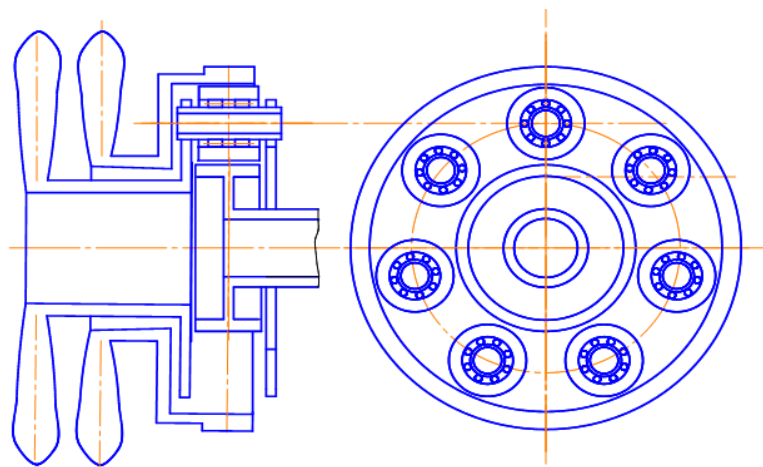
Схема дифференциального редуктора турбовинтовентиляторного двигателя
